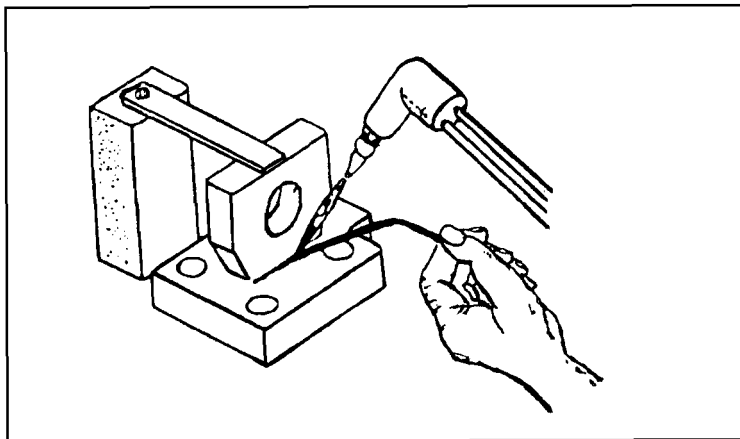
SOLDEO FUERTE O BLANDO CON SOPLETE
